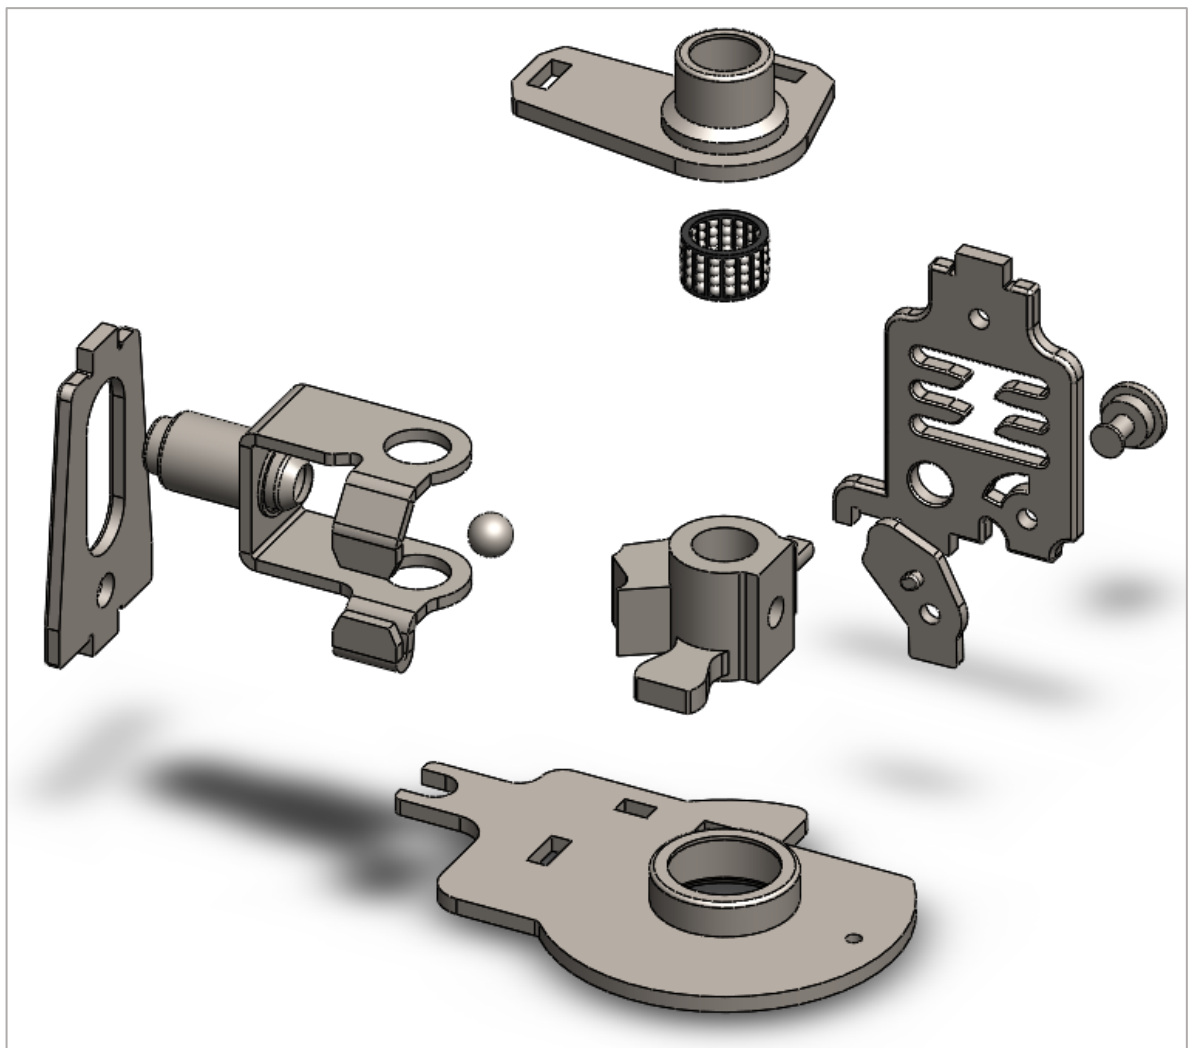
122 Explosionado conjunto interno de la palanca de mando
